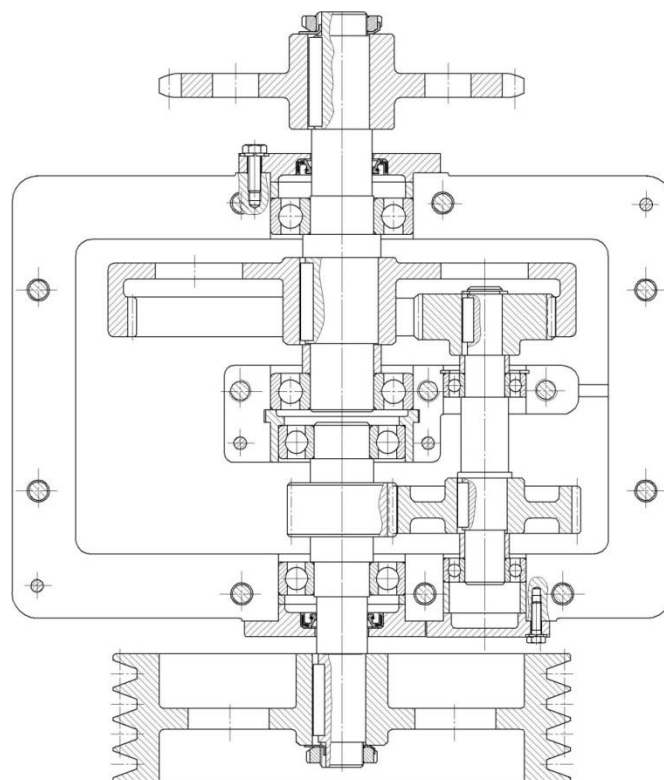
Чертеж редуктора (разрез по плоскости разъема)
